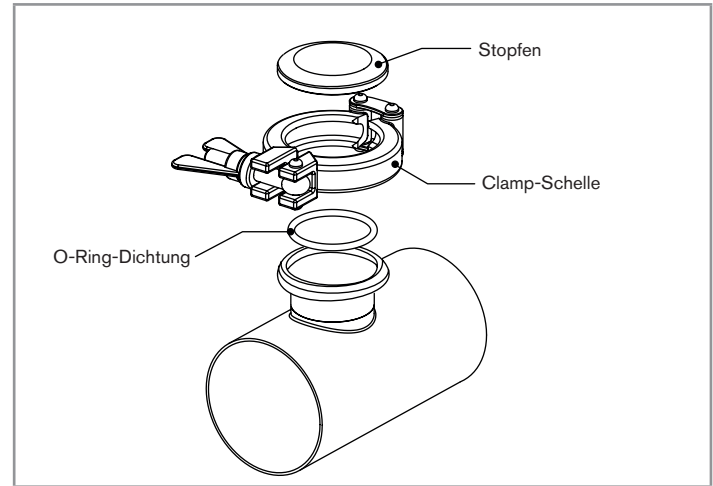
Stopfen, Clamp-Schelle und O-Ring-Dichtung der S020 für Messgeräte mit Clamp-Anschluss
